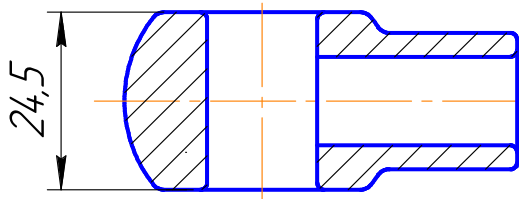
Эскиз отливки для расчета размера полости пресс-формы, образованной наружным размером отливки
